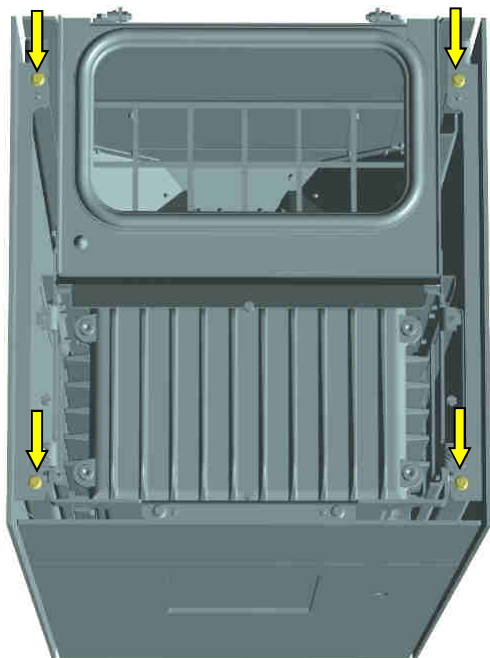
Befestigungsschrauben Seitenverkleidungen
